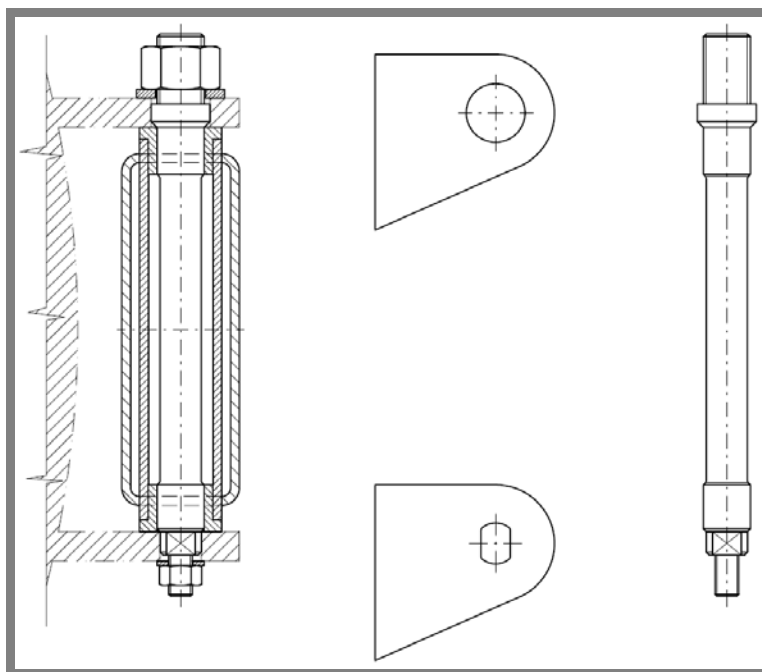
Tvar přední části ramena a rozvinutého plechu
